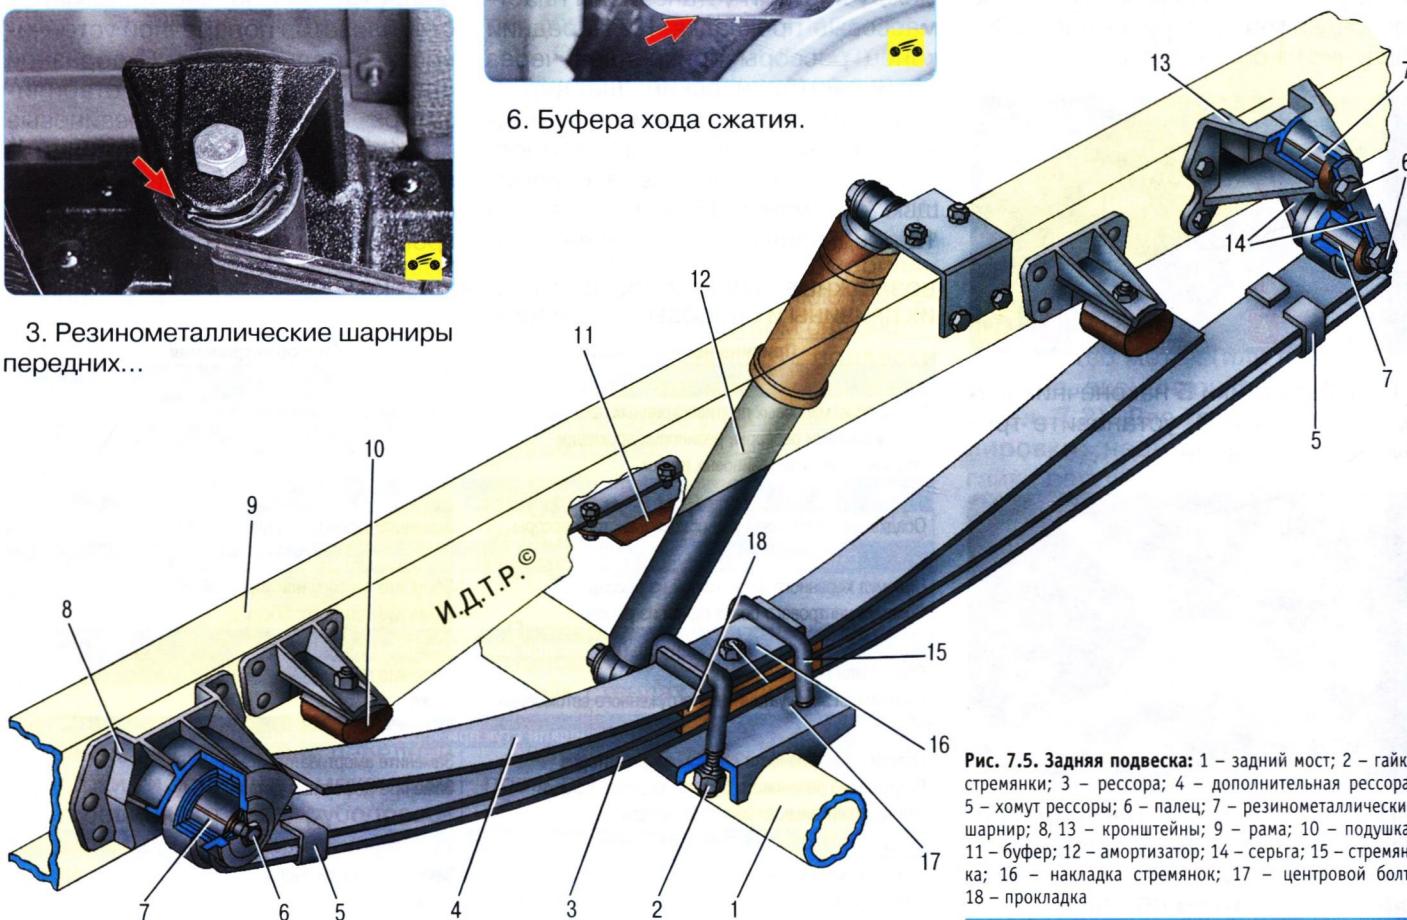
Задняя подвеска: 1 – задний мост; 2 – гайка стремянки; 3 – рессора; 4 – дополнительная рессора; 5 – хомут рессоры; 6 – палец; 7 – резинометаллический шарнир; 8, 13 – кронштейны; 9 – рама; 10 – подушка; 11 – буфер; 12 – амортизатор; 14 – серга; 15 – стремянка; 16 – накладка стремянок; 17 – центровой болт; 18 – прокладка
